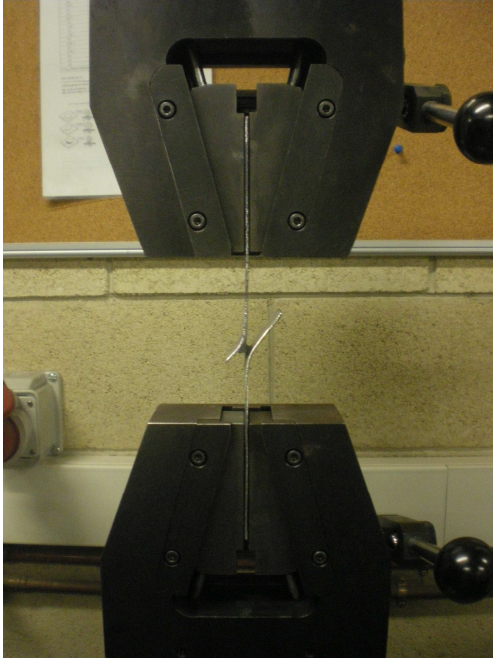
y 6.4 Detalle estado final de probeta punto ok tras ensayo de tracción
